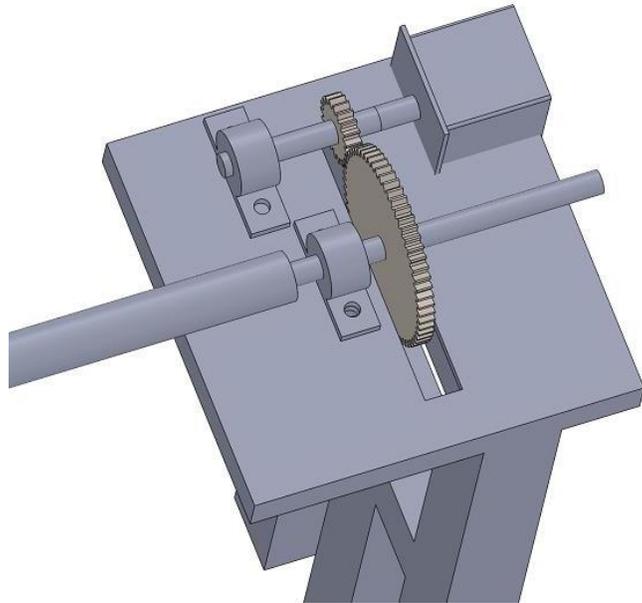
Acercamiento del sistema de transmisión por engranaje del CCP.
